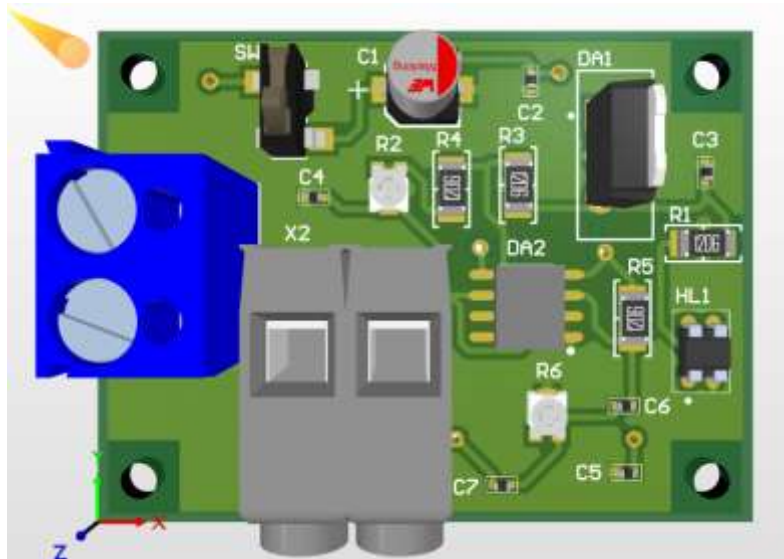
Тривимірна візуалізація друкованої плати з розробленим корпусом для розміщення підсистеми (вид зверху)
